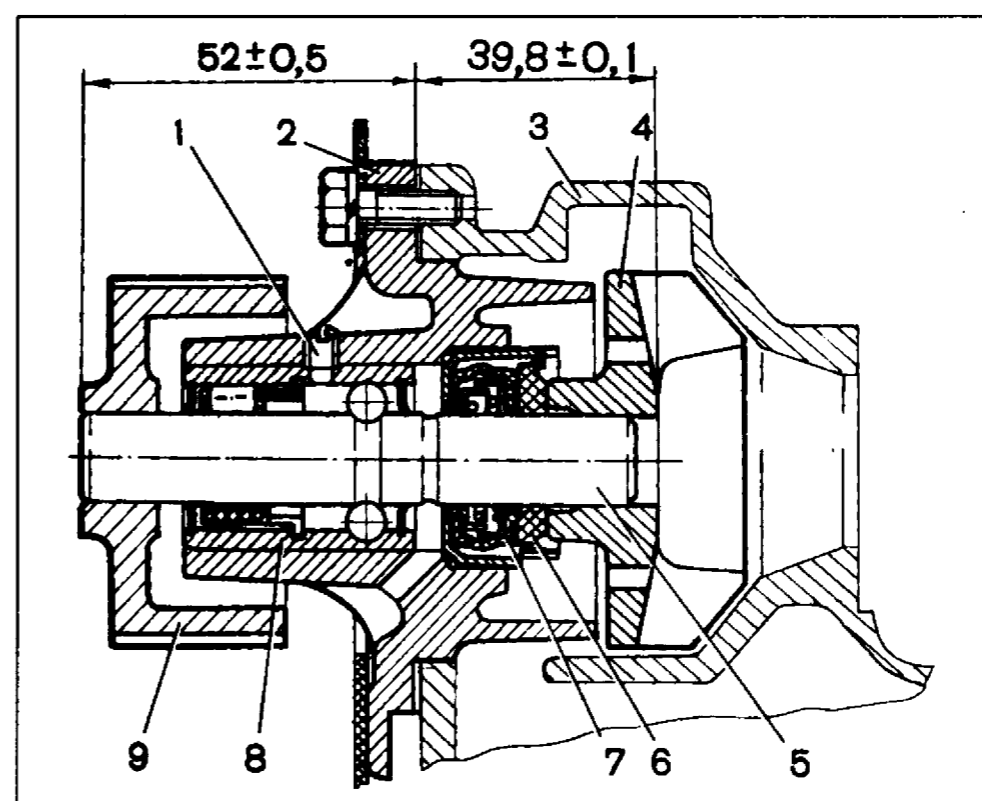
Насос охлаждающей жидкости с контрольными размерами для сборки:
